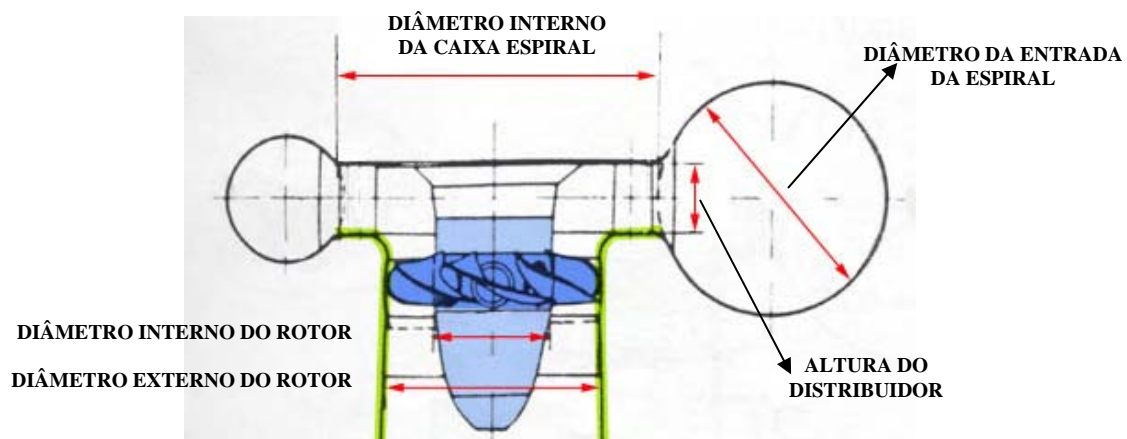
Dimensões do rotor e caixa espiral da turbina Kaplan
